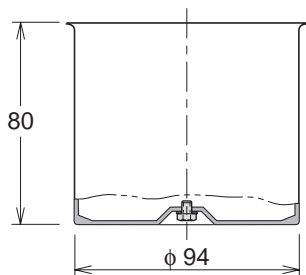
Tanktyp "A"; 0,46 l (0,21 l användbart); aluminium.
